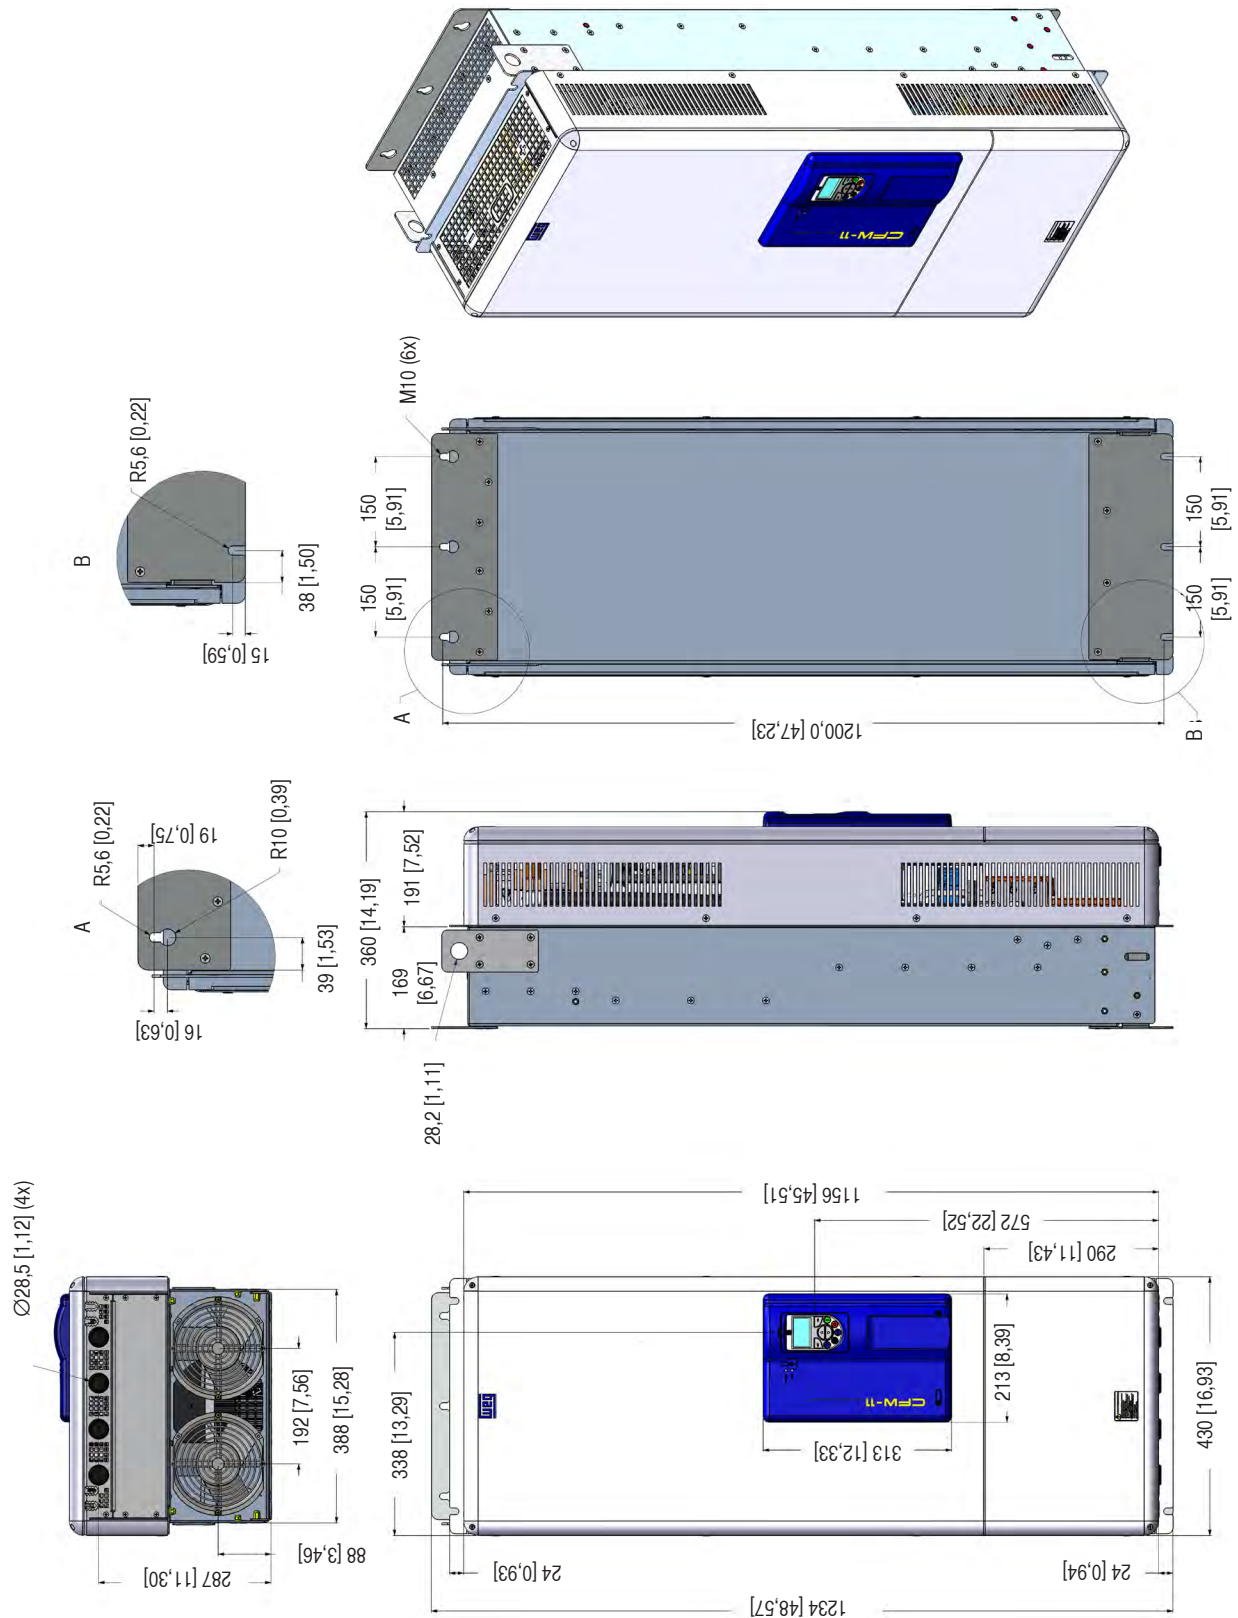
Размеры корпуса F, мм [дюйм.]
